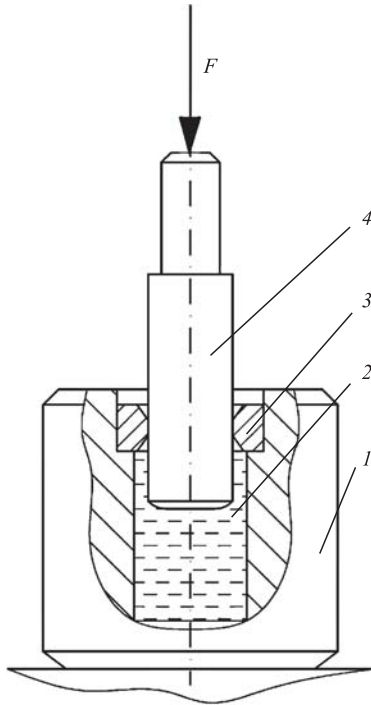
Конструкция приспособления для ОППД со сжатием образцов-заготовок:
